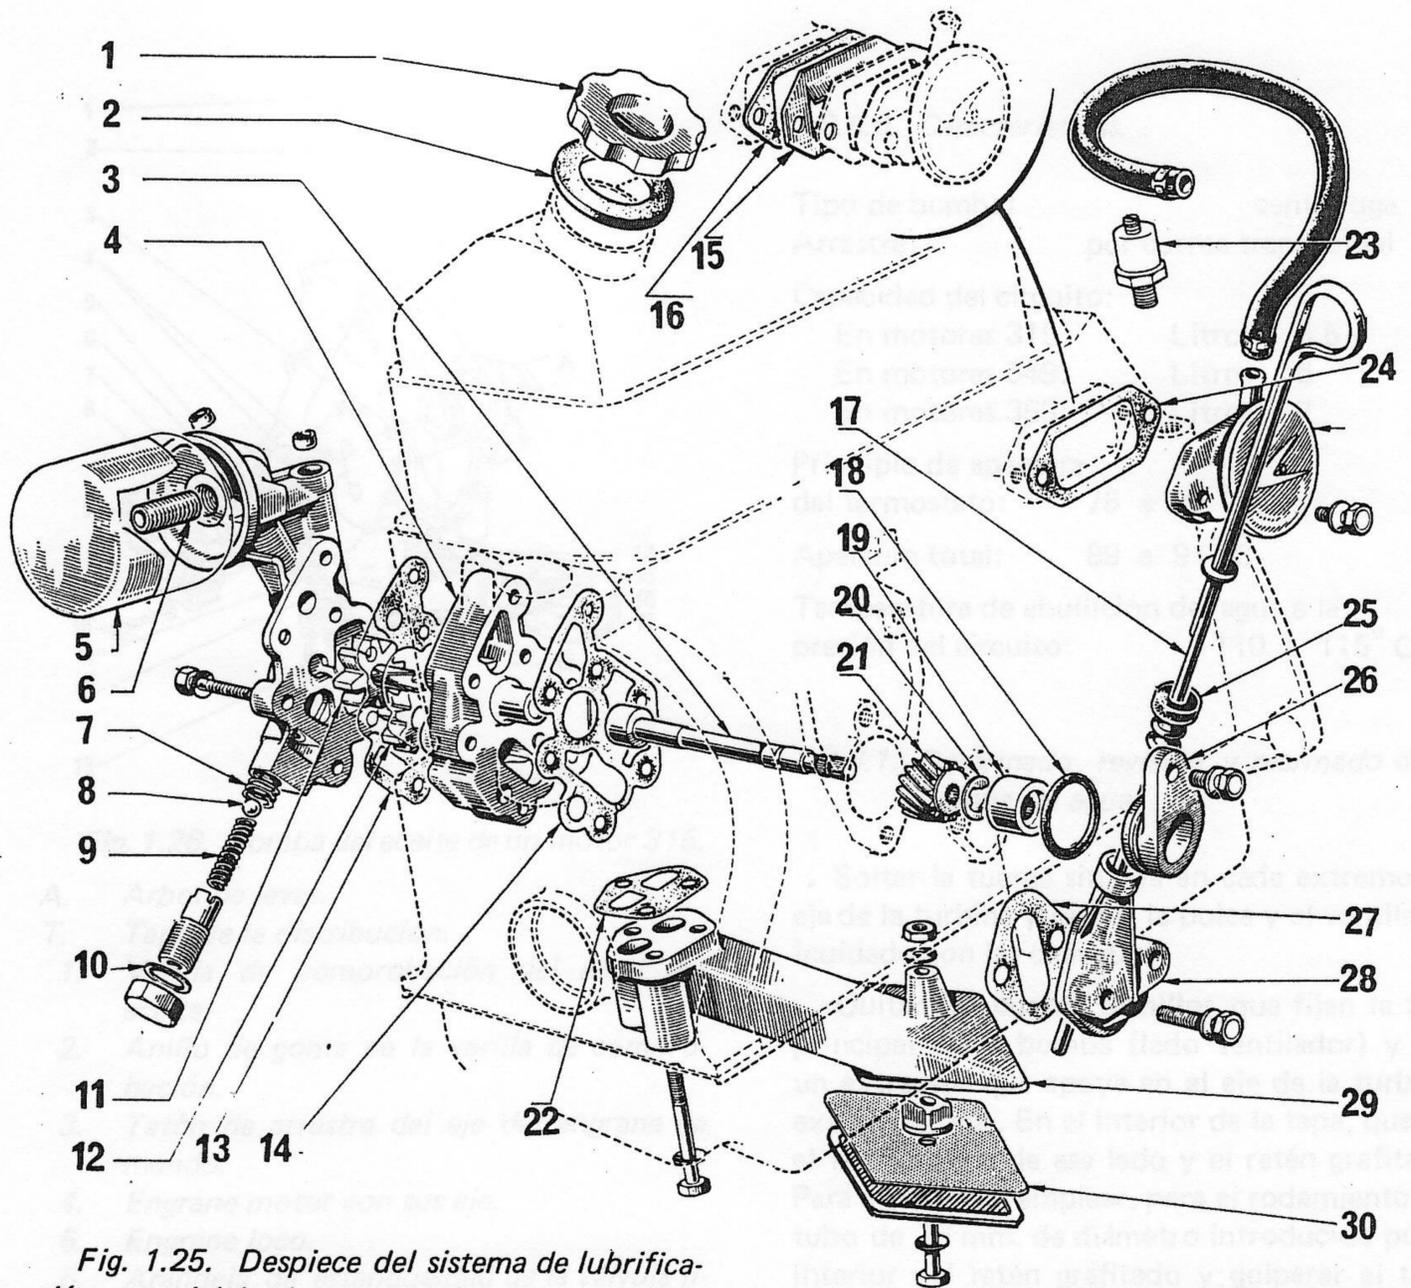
Despiece del sistema de lubricación y reciclaje de vapores de un motor 349.
